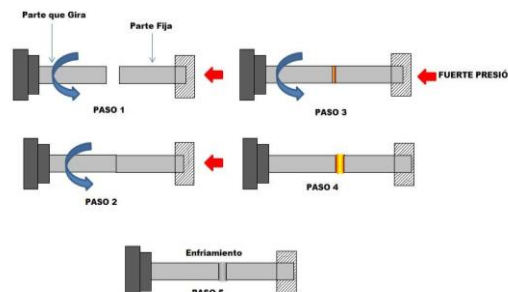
Esquema de Funcionamiento de Soldadura por Fricción
